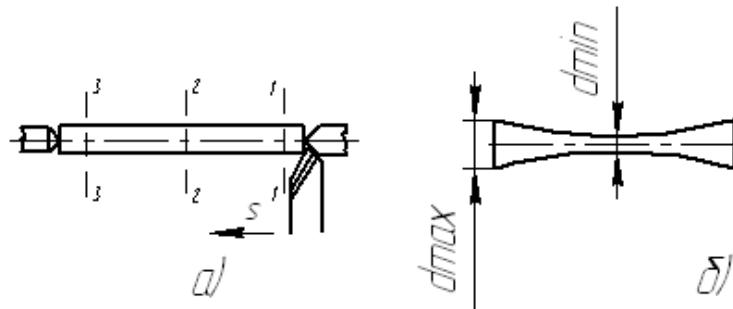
Закріплення заготовки у центрах (заготовка більш жорстка, ніж верстат)
